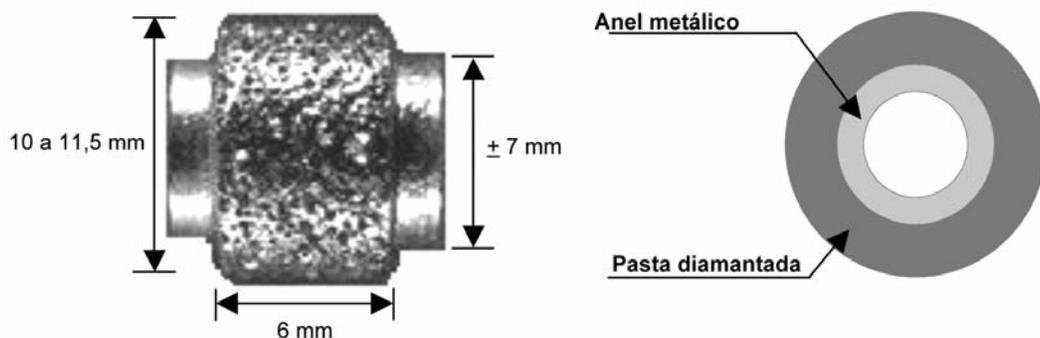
Dimensões padrão de uma pérola diamantada.
